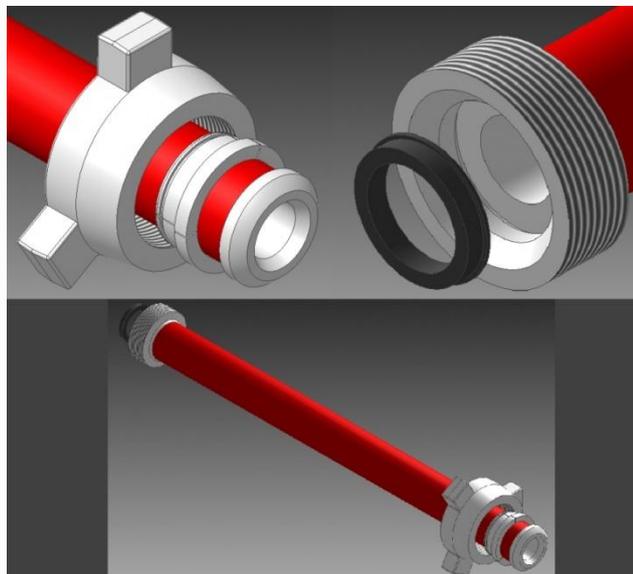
Pup Joint (FUENTE: XI'AN Kingwell OILFIELD MACHINERY CO., LTD)
